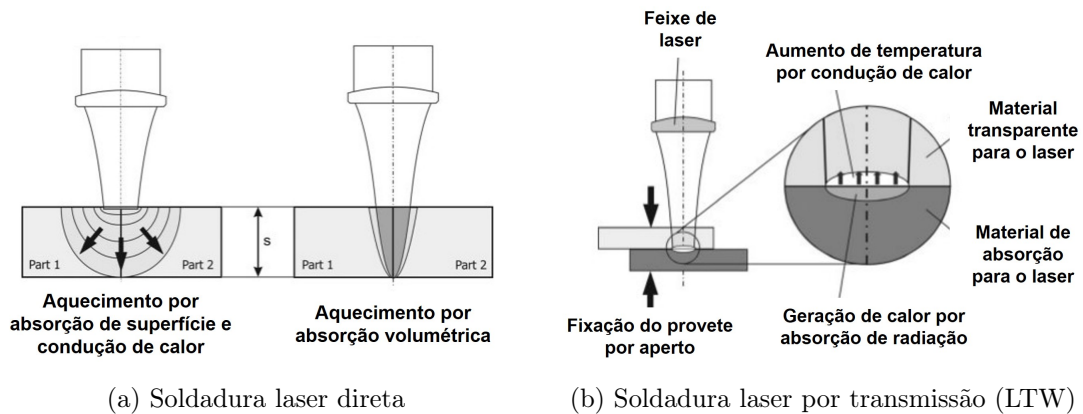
Processos de soldadura laser. Adaptado de [13].
